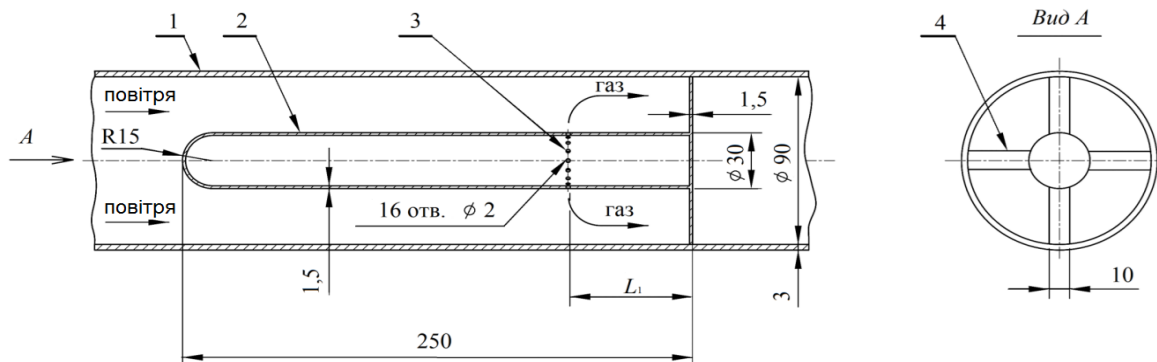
Поздовжній переріз циліндричного стабілізаторного пальника з пластинчастими турбулізаторами потоку: 1 – циліндричний канал; 2 – циліндричний стабілізатор полум'я; 3 – газоподаючі отвори; 4 – пластинчастий турбулізатор
